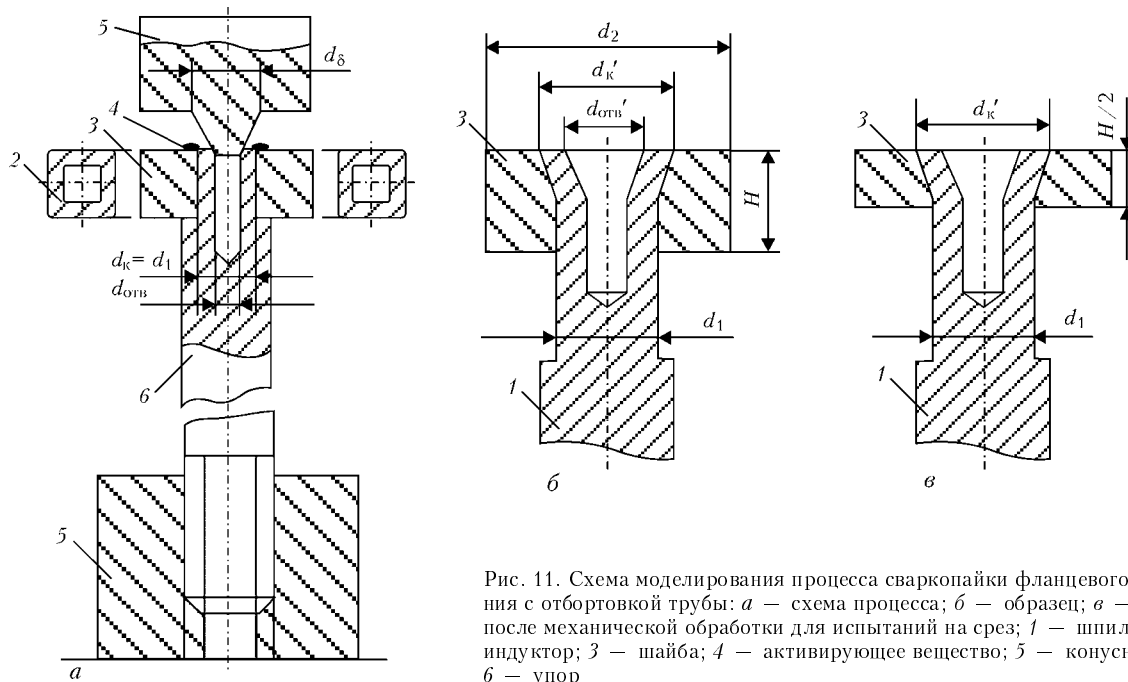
Схема моделирования процесса сваркопайки фланцевого соединения с отбортовкой трубы: а — схема процесса; б — образец; в — образец после механической обработки для испытаний на срез; 1 — шпилька; 2 — индуктор; 3 — шайба; 4 — активирующее вещество; 5 — конусный боек; 6 — упор
